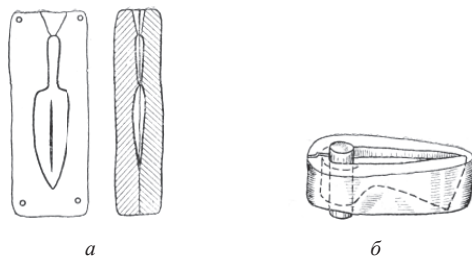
Древние литейные формы, изготовленные из камня: *а* – форма для отливки кинжала; *б* – форма для отливки топора
